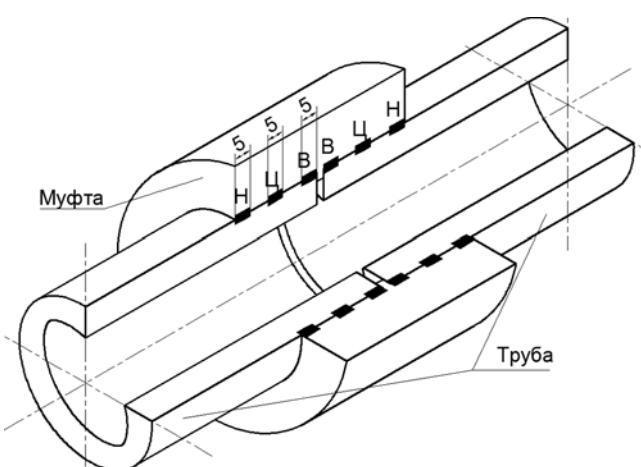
Схема разделения сварного раструбного соединения на три зоны: Н — наружная; Ц — центральная; В — внутренняя
